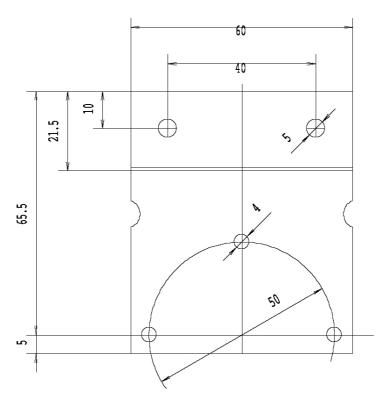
Габаритные и присоединительные размеры монтажной скобы.
